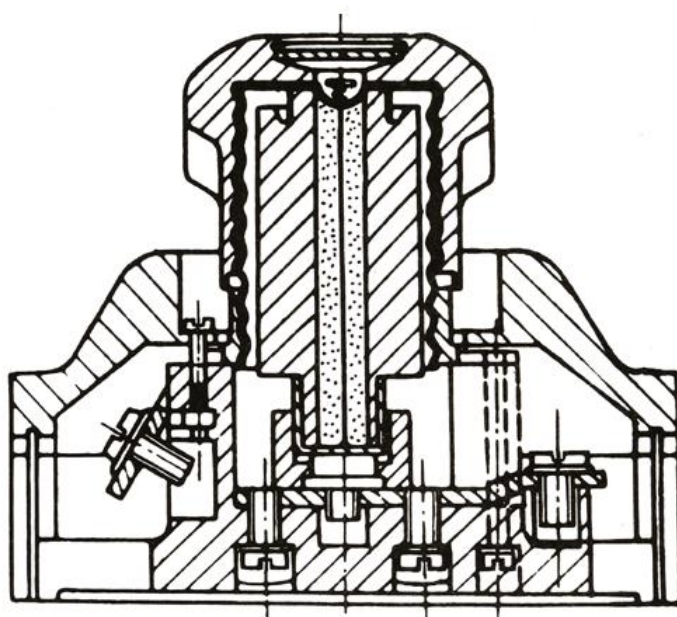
Konstrukční provedení pojistky jedno a dvoelementové (konstrukce Bussman)
